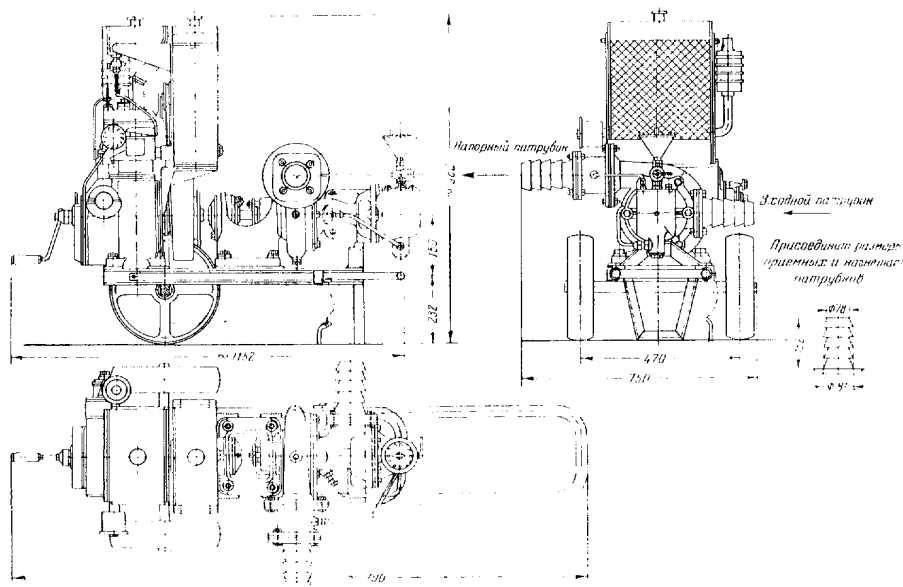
Габаритный чертеж мотопомпы модели БМП-80^а
